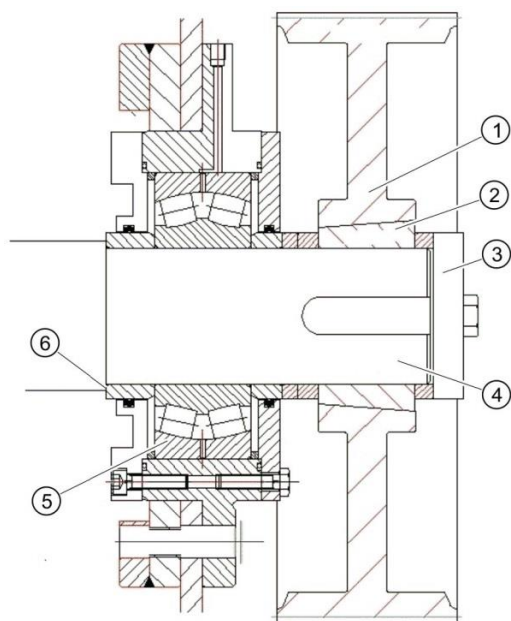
Вал, подшипник и ременный шкив в разрезе
